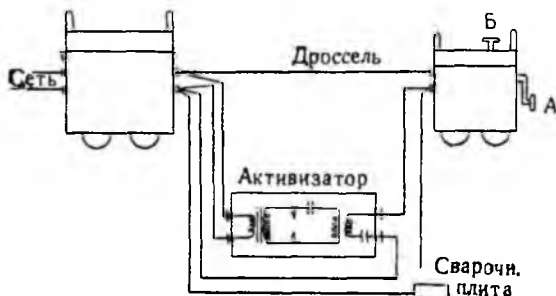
Схема включения сварочного трансформатора СТЭ-22.
